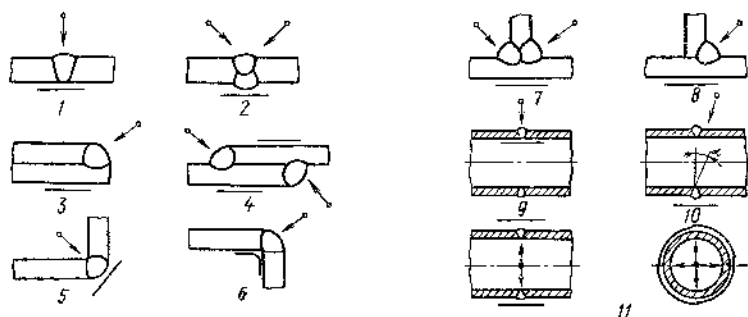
Схемы (1—11) контроля сварных соединений
